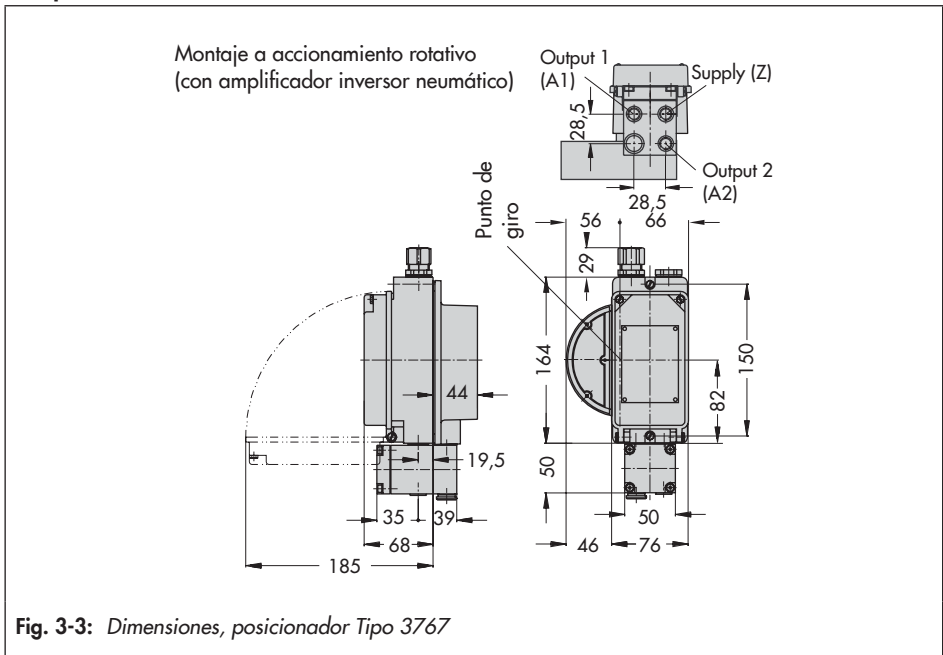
Dimensiones, posicionador Tipo 3767
